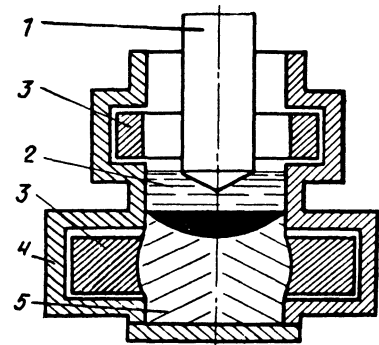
Схема ЭШЛ с приплавлением закладных элементов отливки: 1 - расходный электрод; 2 - жидкий шлак; 3 - закладные элементы; 4 - форма; 5 - отливка
